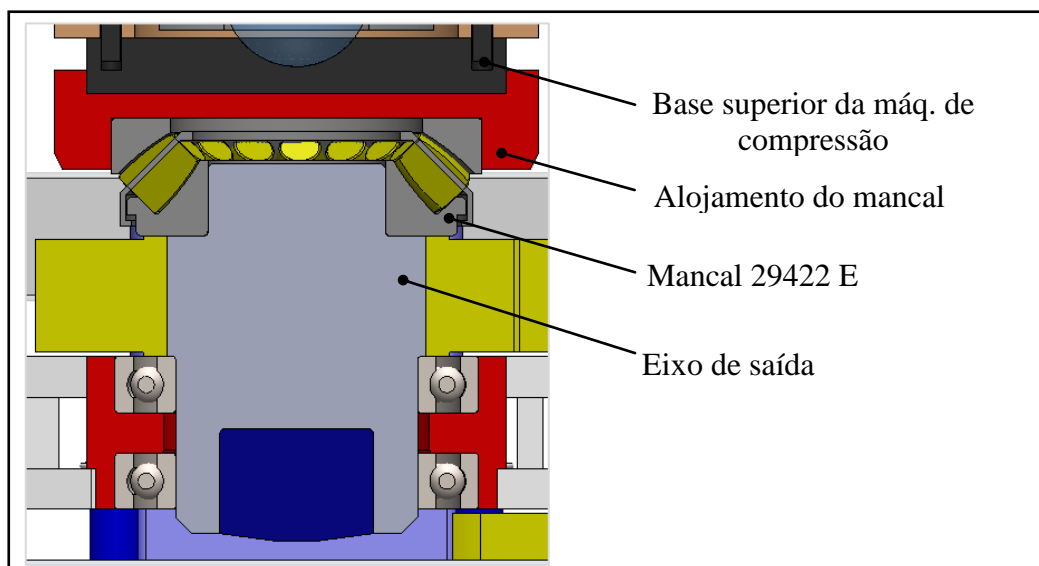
Vista esquemática em corte de seção transversal do conjunto de montagem do eixo de saída
